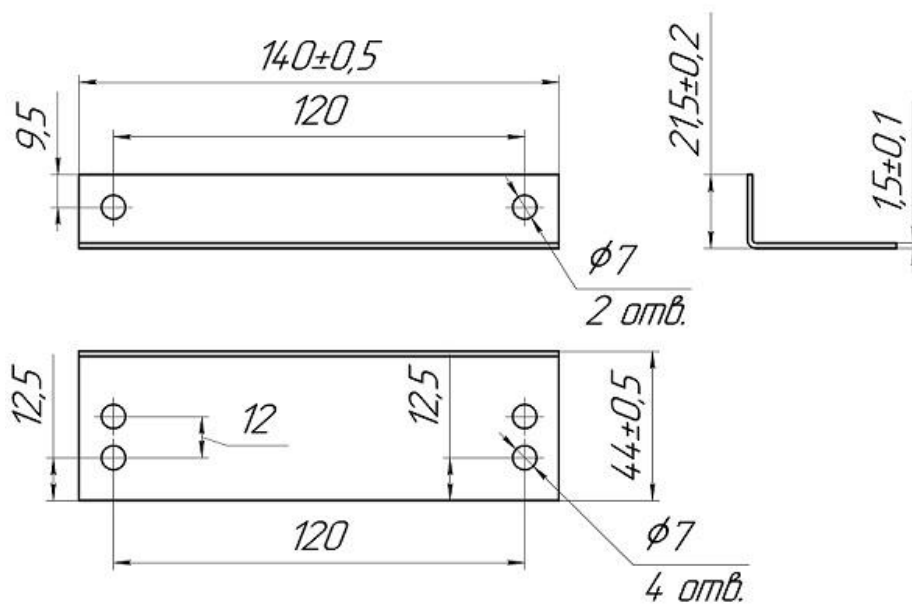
Габаритные и присоединительные размеры кронштейна К-ДПМ-1
